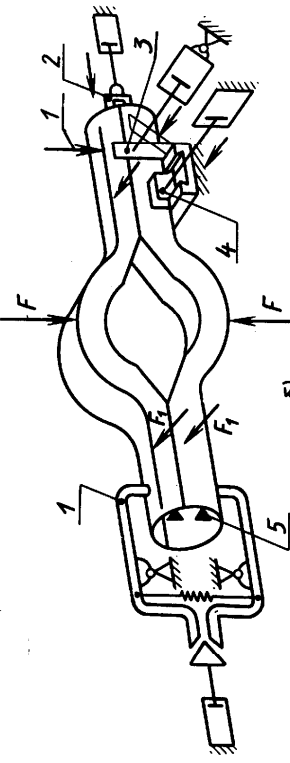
Схема операций сборки и сварки на ступе I (см. рис. 3)
